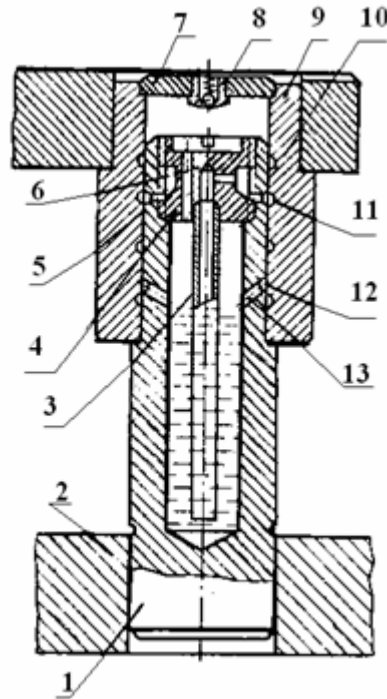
Конструкция направляющих элементов штампа с принудительной подачей смазки
